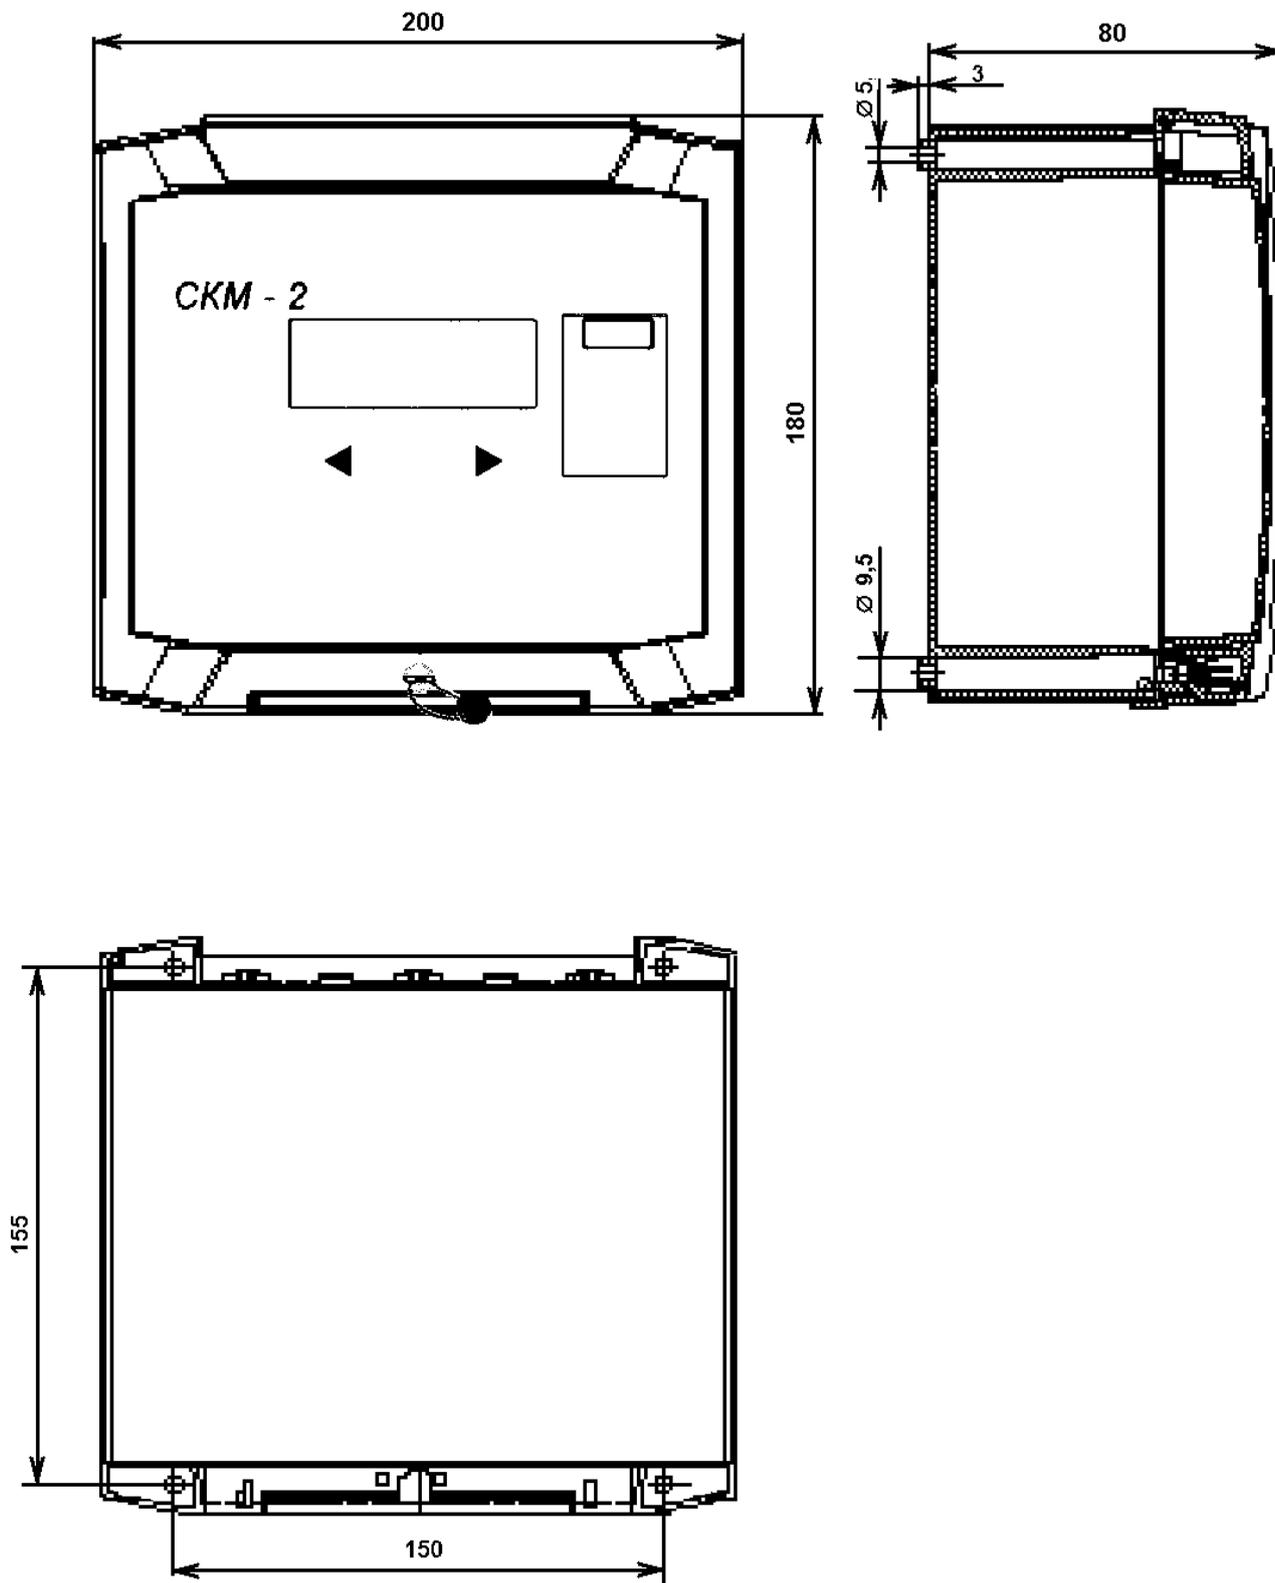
Габаритные и установочные размеры вычислителя многоканального (корпус Borla)
